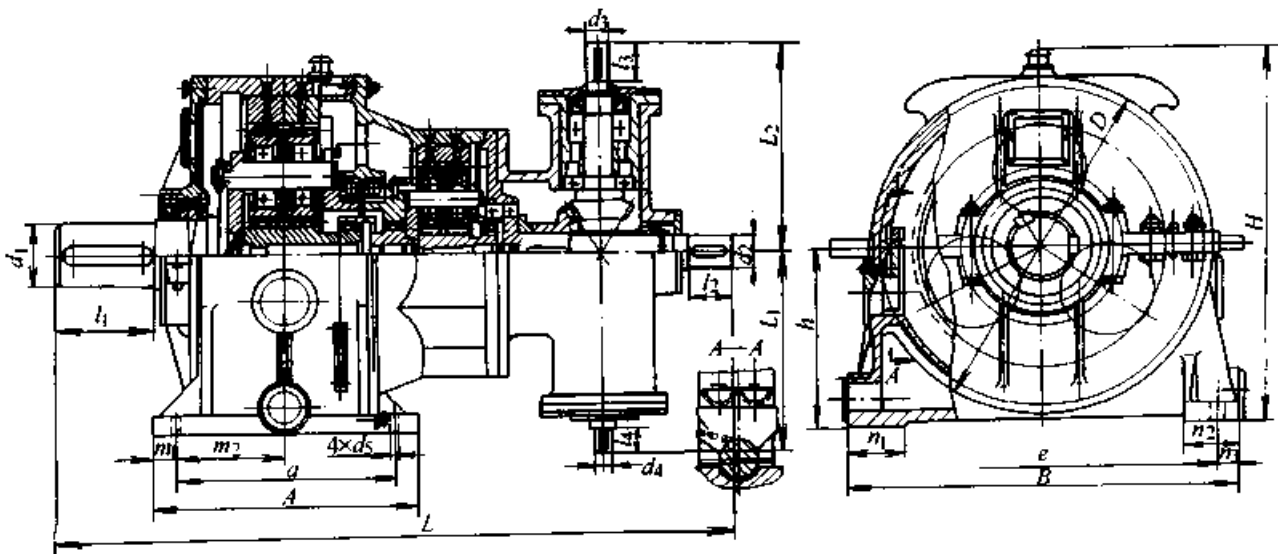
NGW-S 型直交行星齿轮减速器结构
